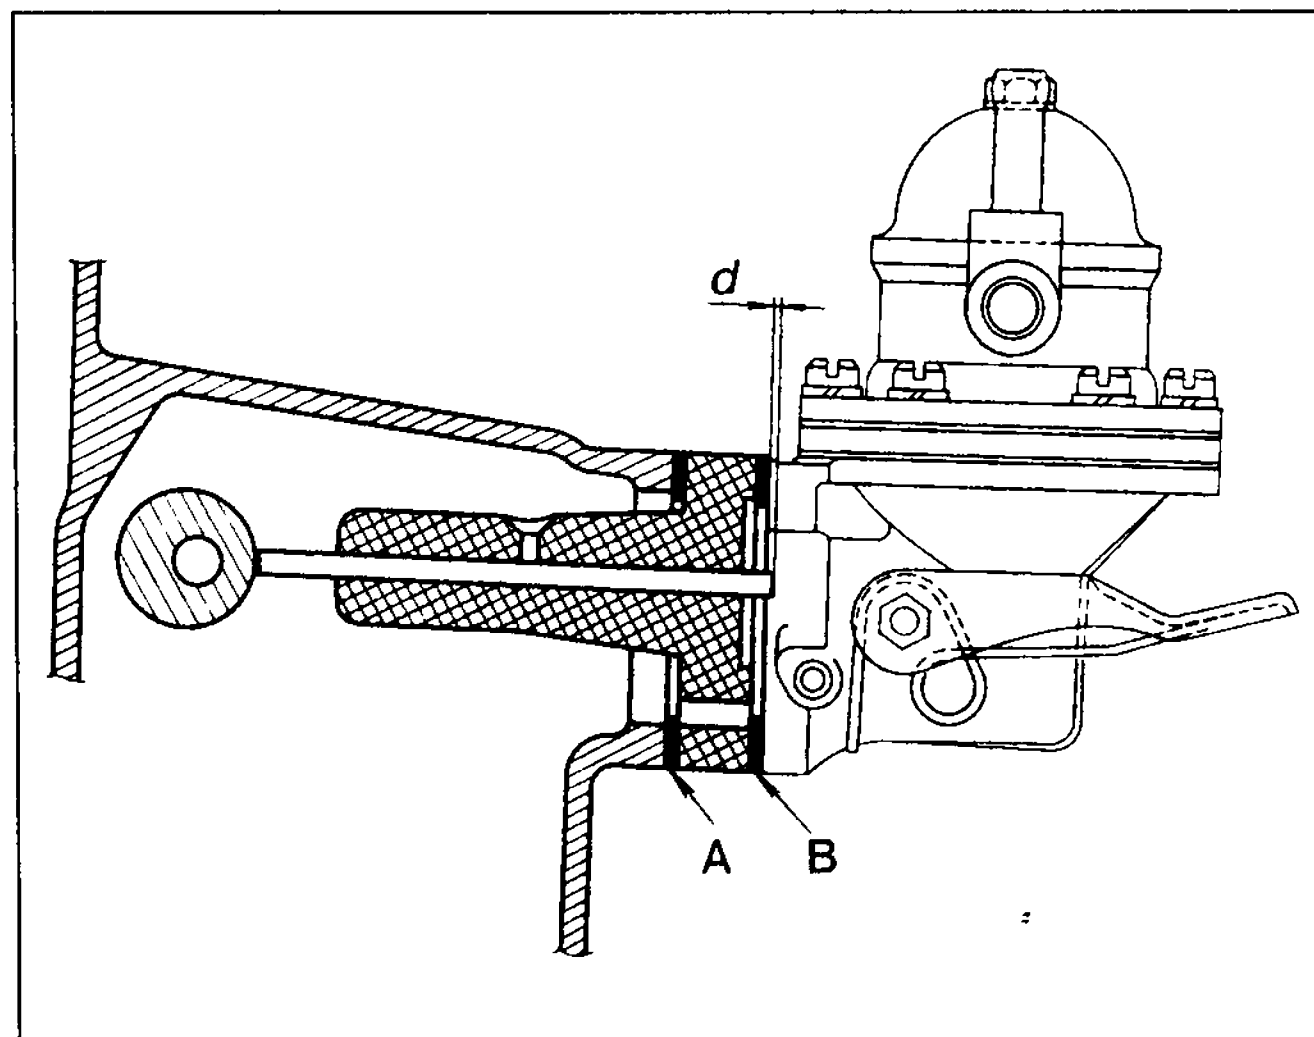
Схема для контроля и регулировки выступания толкателя привода насоса:
